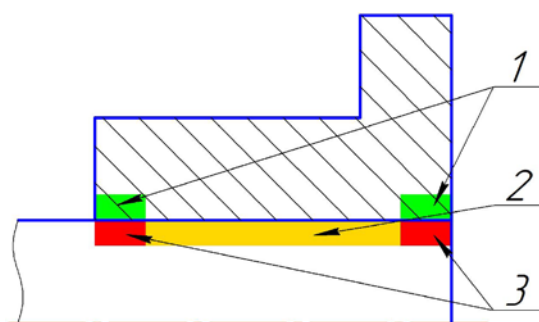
КЕІП на поверхнях з'єднання «півмуфта – вал»:
